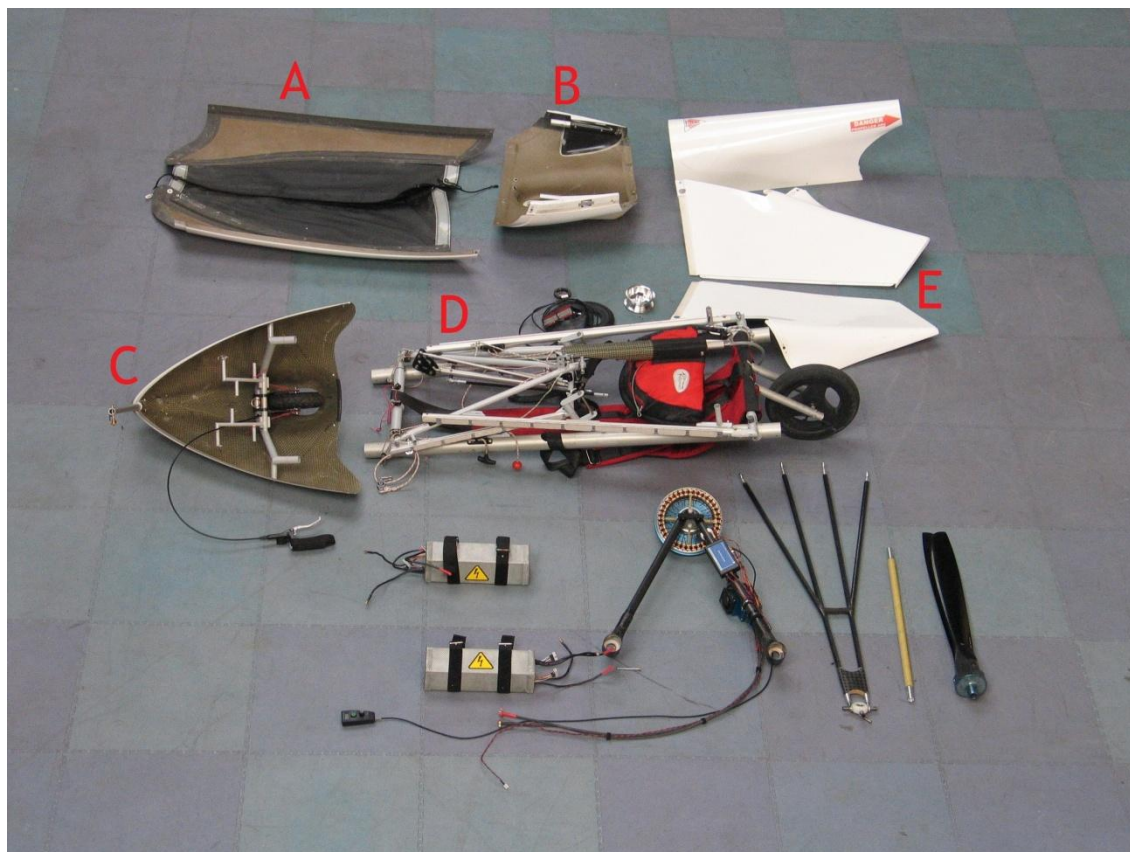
Componentes da fuselagem do Swift'light motorizado: (A) Carenagem inferior central original; (B) Carenagem inferior traseira; (C) Carenagem inferior dianteira frontal, com estrutura do patim e roda dianteira implementada; (D) Estrutura da carenagem original dobrada, é visível o foguete reorientado e a sua "rampa"; (E) Faces laterais da carenagem traseira baseadas na carenagem original.
